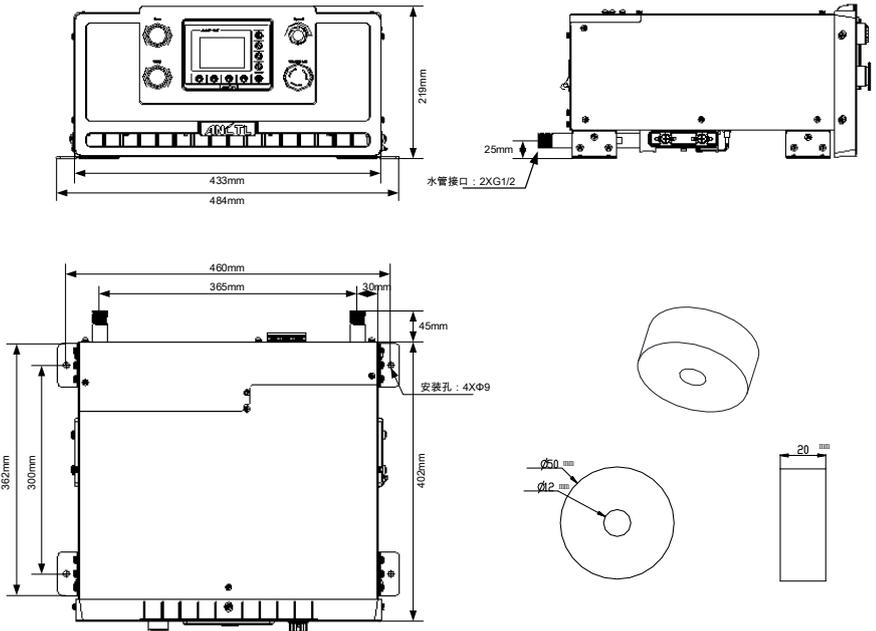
外型尺寸安装尺寸及减震垫示意图 (AWD100-4T0501~ AWD100-4T1804)
